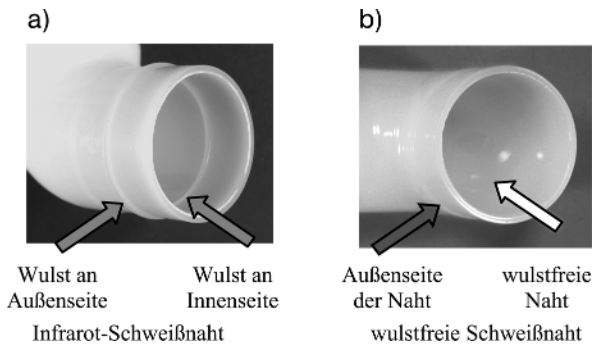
Schweißnähte an Kunststoffrohren:
